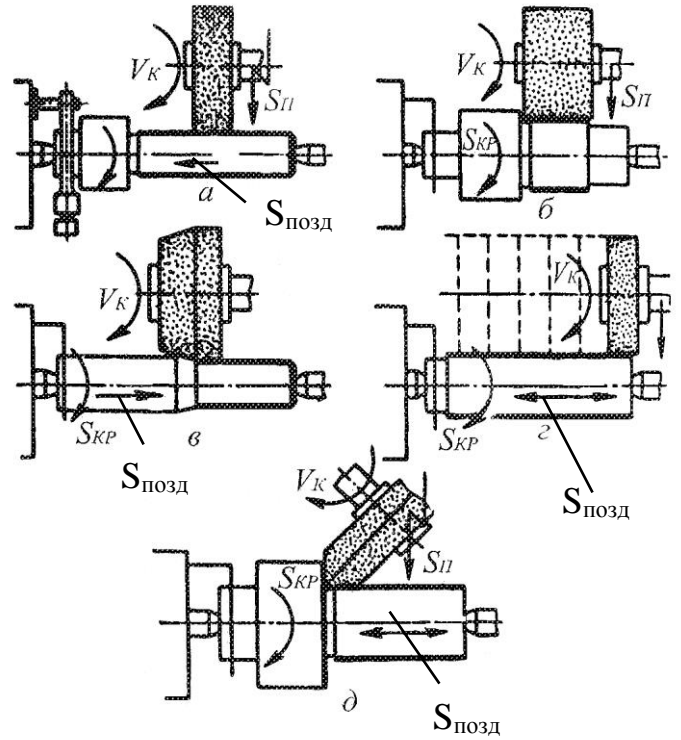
Схеми обробки заготовок на круглошліфувальних верстатах
